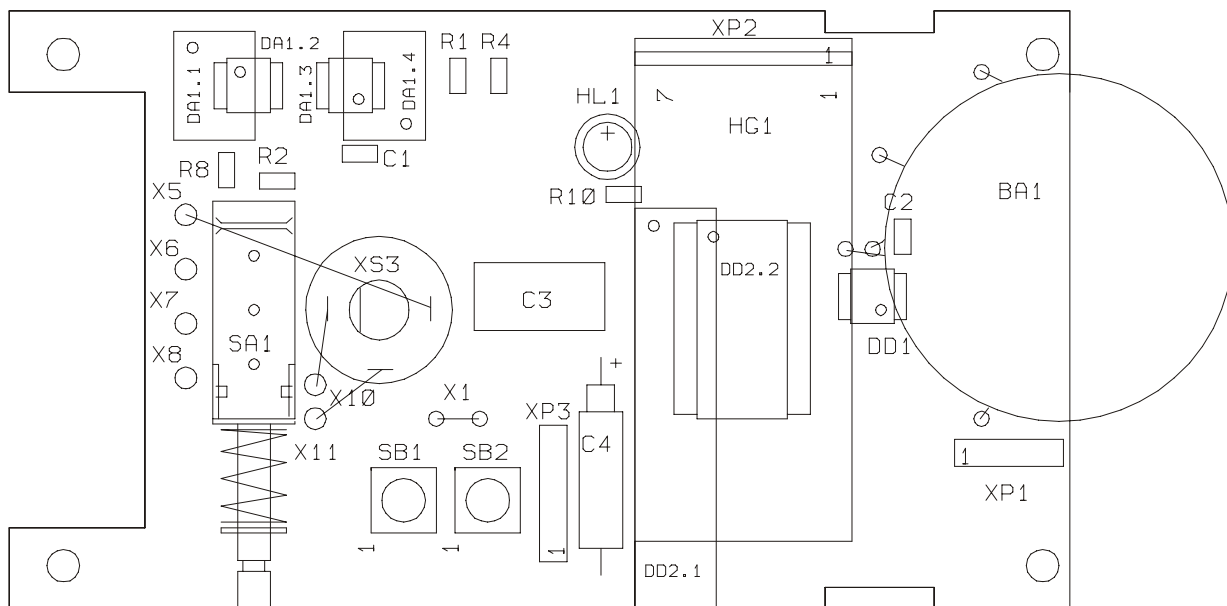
Сборочный чертеж платы обработки ФП11.3. Сторона монтажа.
